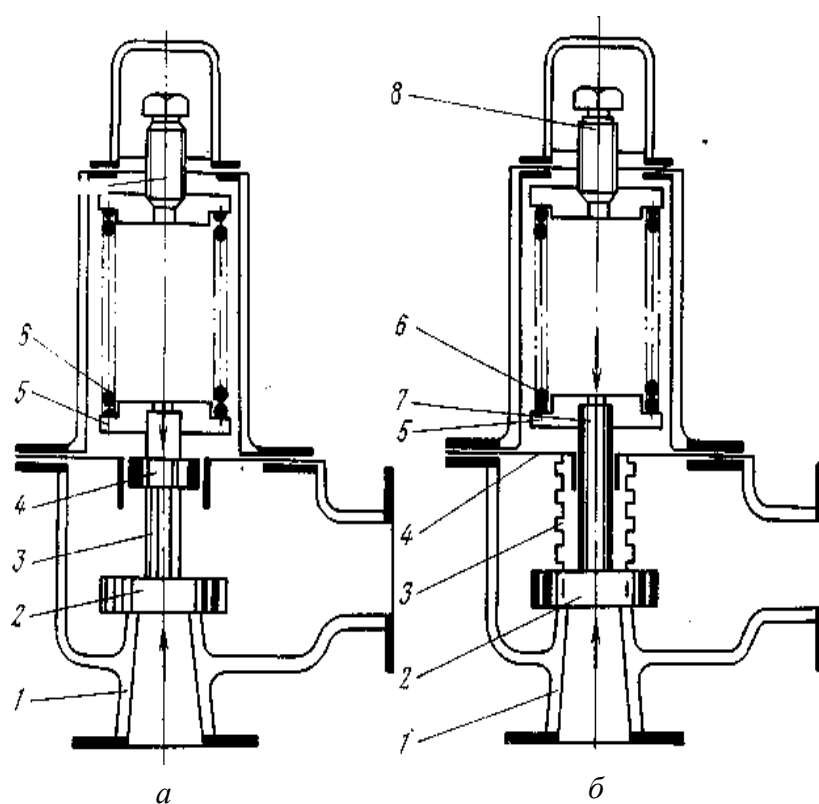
Уравновешенный пружинный предохранительный клапан:
